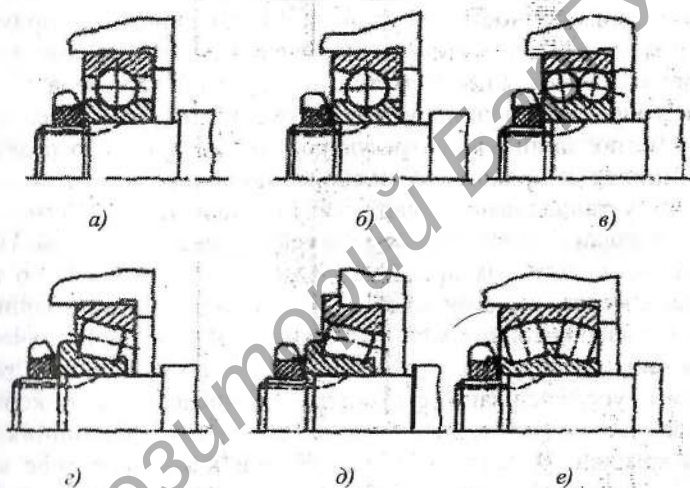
Конструкции опоры [9, с. 109]
